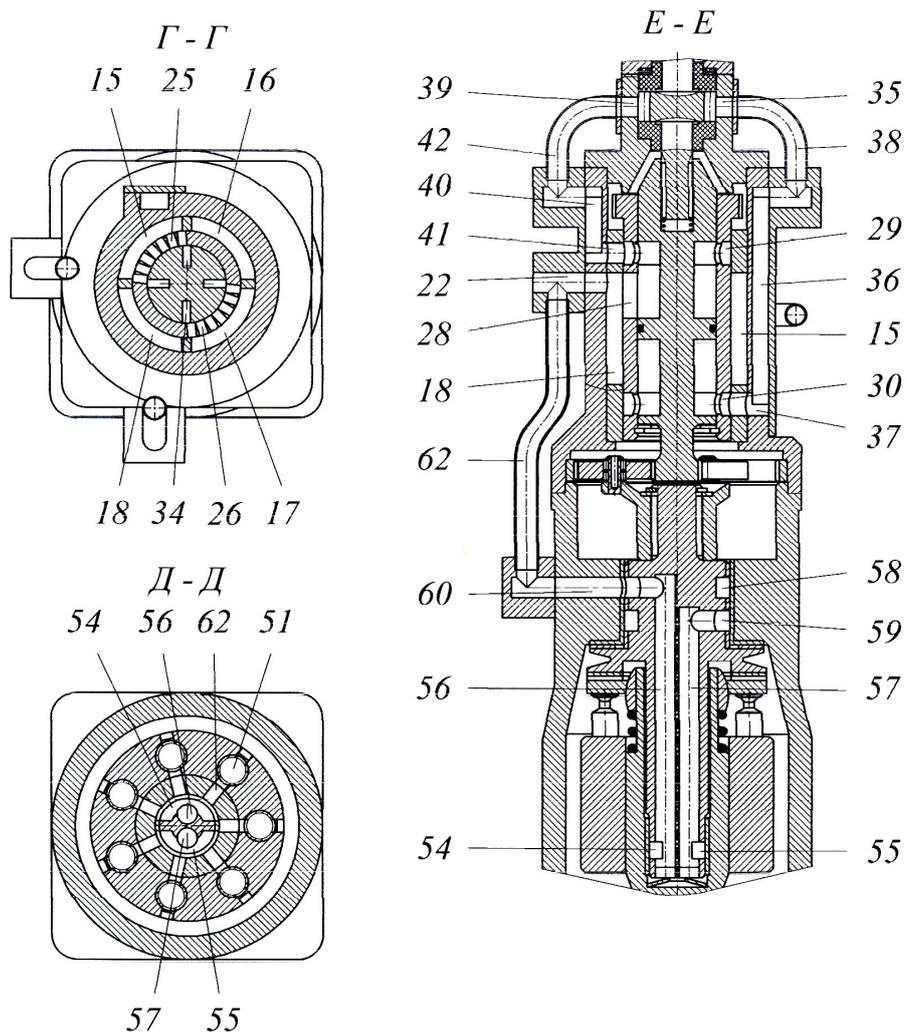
(продолжение). ОГП с планетарным редуктором в линии связи приводного вала и наклонной шайбы гидромотора
